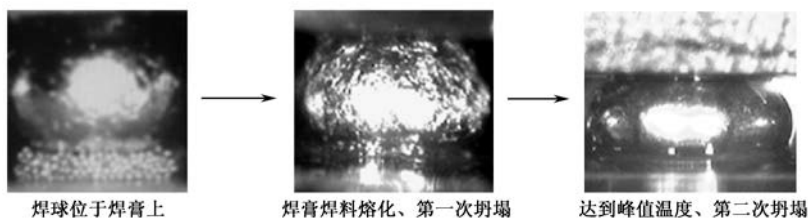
P BGA 再流焊接过程的实时录像
